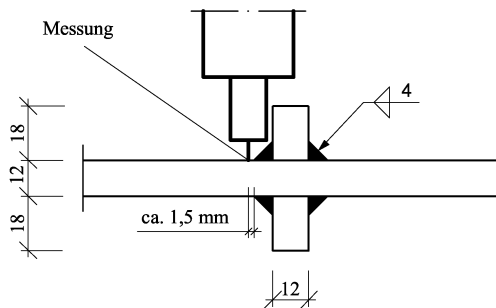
Abstand der Bohrlochmitte vom Schweißnahtübergang
